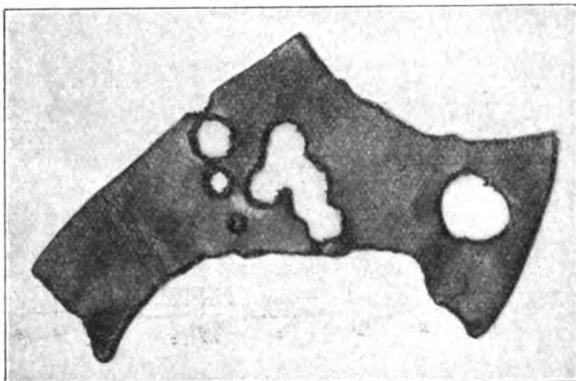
Stück einer zerfallenen Orgelpfeife aus der Kirche zu Ohlau in Schlesien.
